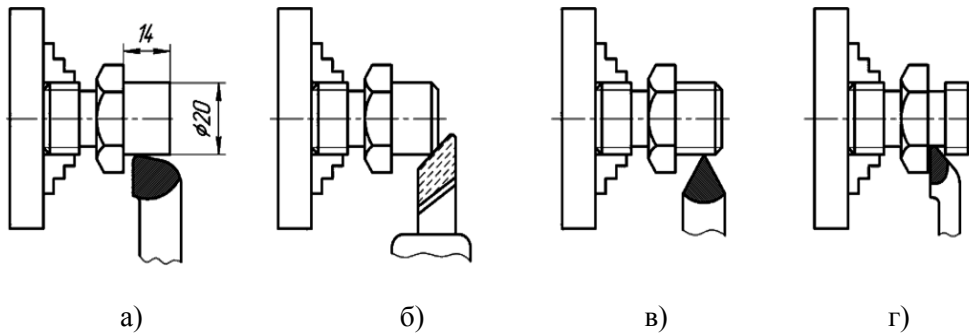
Етапи обробки поверхонь правої різьбової частини штуцера
